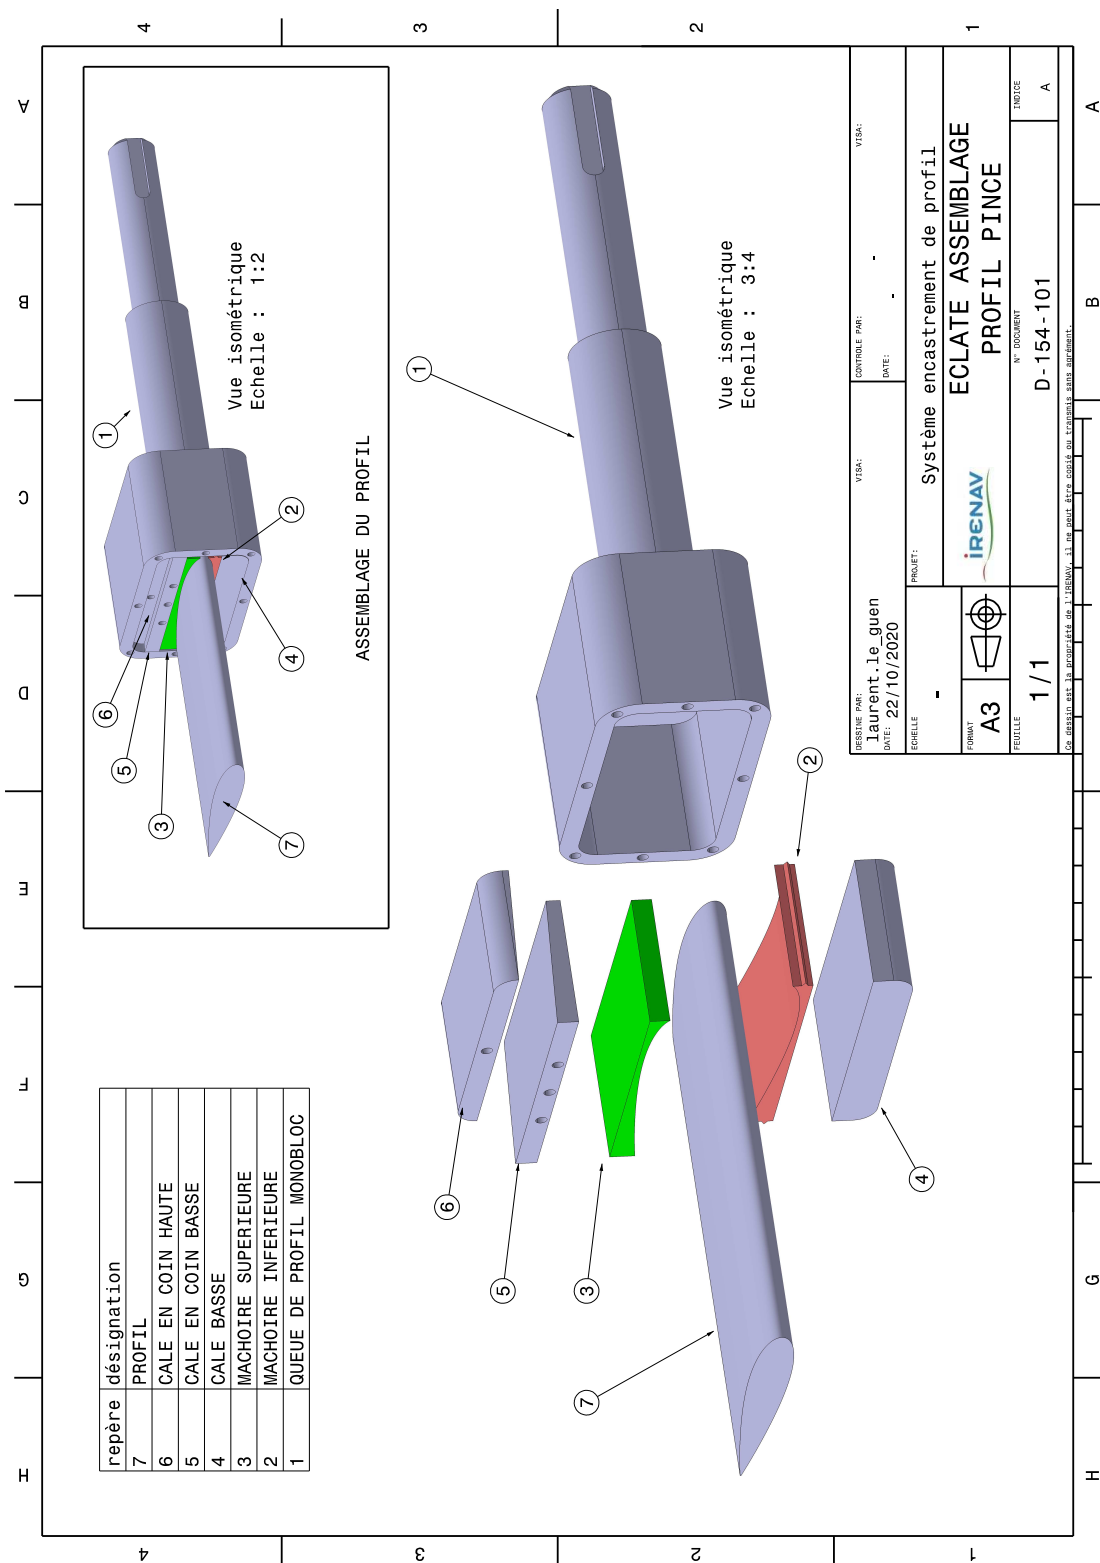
Plan du système d'encastrement du profil sur sa queue de mesure
